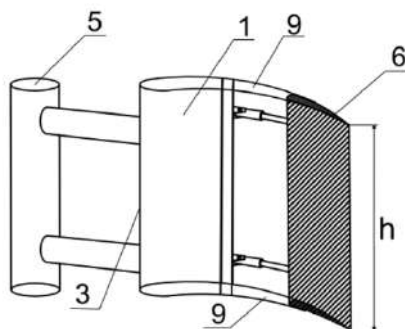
Вид устройства со стороны рабочей поверхности лопасти
